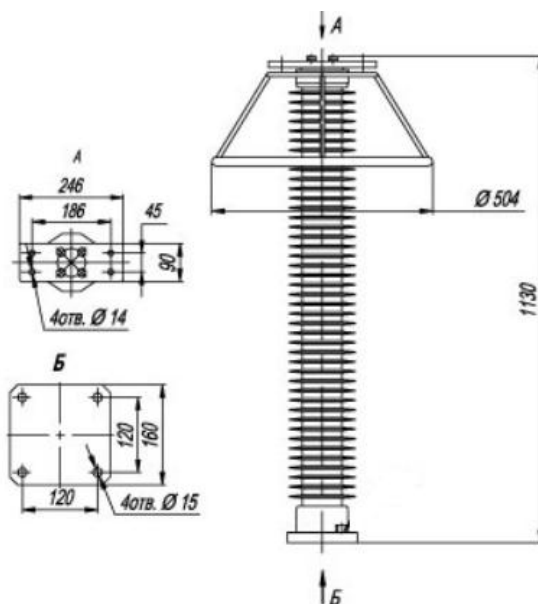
Нелінійний обмежувач перенапруги в полімерному корпусі опорного виконання
